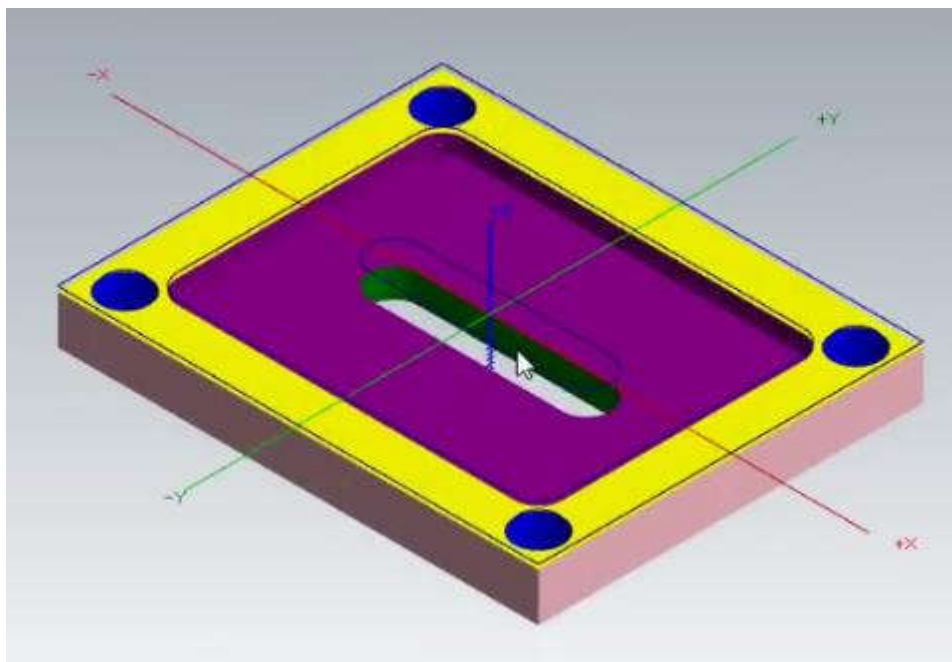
Présentation en 3D de la pièce prismatique sous MasterCam
